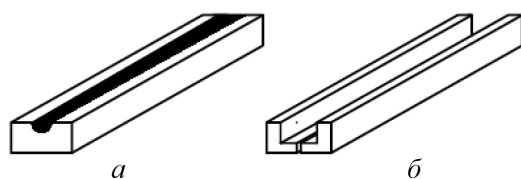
Фрезерование и распиловка брусков: *а* – бруски с ядровой гнилью; *б* – элементы уголкового профиля
